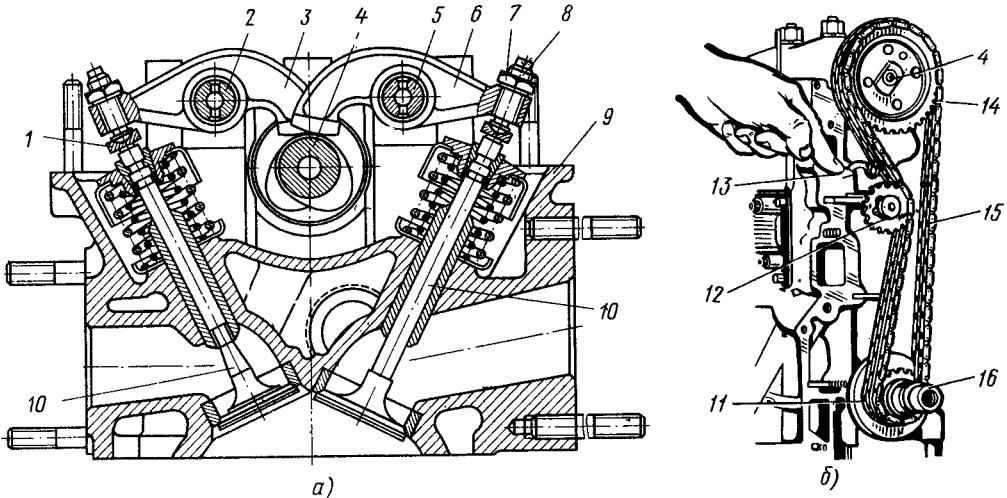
Газораспределительный механизм с верхним расположением распределительного вала («Москвич-412»):
